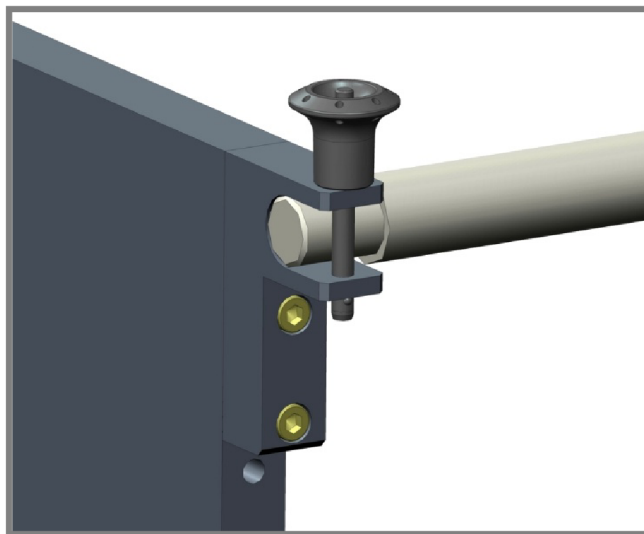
Montážní stroj firmy SOMA [autor]
